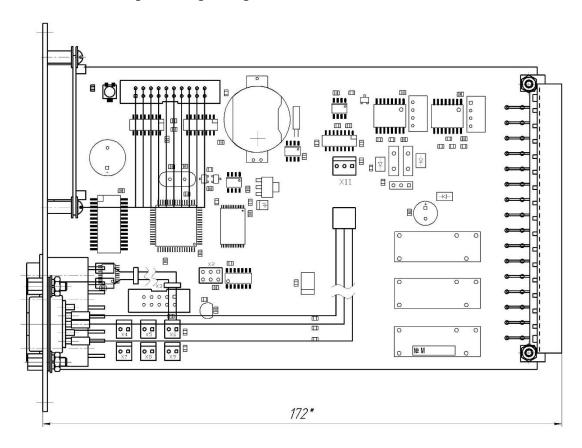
Габаритные и установочные размеры МАП-СГМ-110/D.
